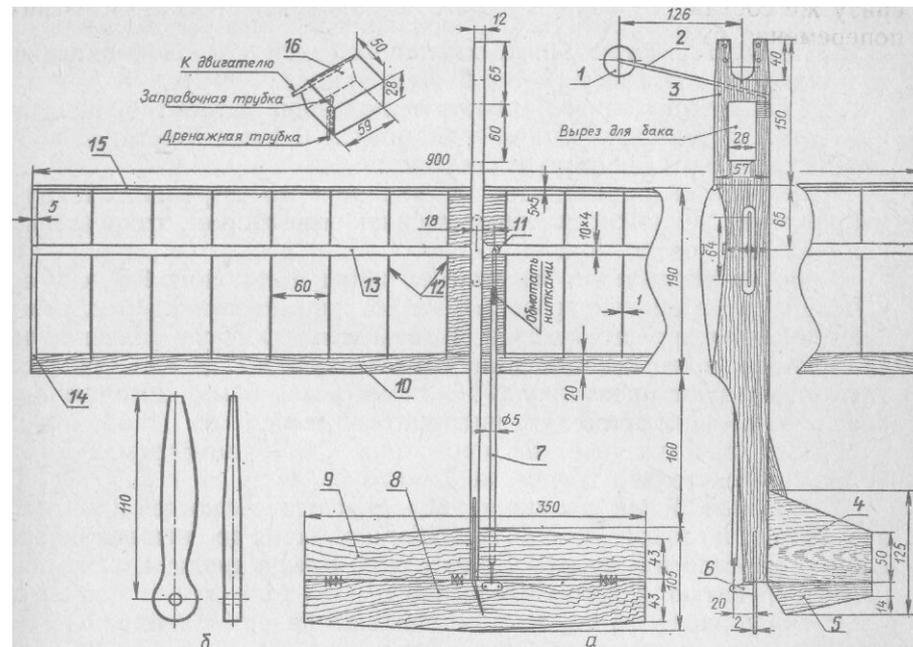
Кордовая учебно-тренировочная модель самолета (а) и шаблон винта (б): 1 — колесо; 2 — стойка шасси; 3 — фюзеляж; 4 — киль; 5 — руль направления; 6 — кронштейн руля высоты; 7 — тяга; 8 — руль высоты; 9 — стабилизатор; 10 — задняя кромка; 11 — качалка; 12 — нервюра; 13 — лонжерон; 14 — законцовка; 15 — передняя кромка; 16 — топливный бак.
